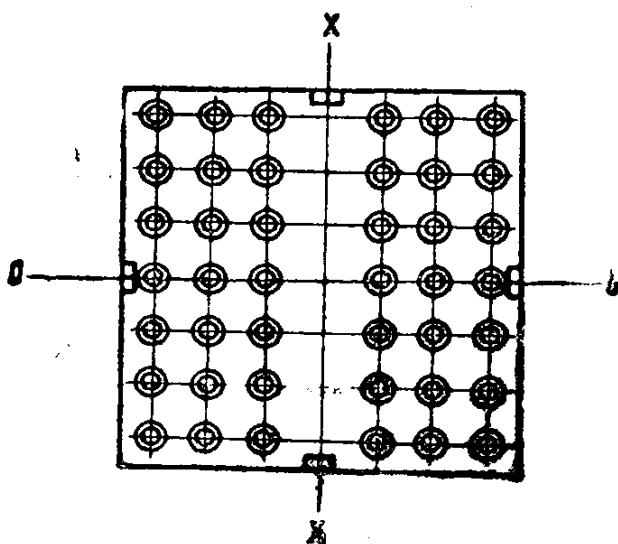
Эталон для сверления отверстий в кондукторах типа ЛП.
